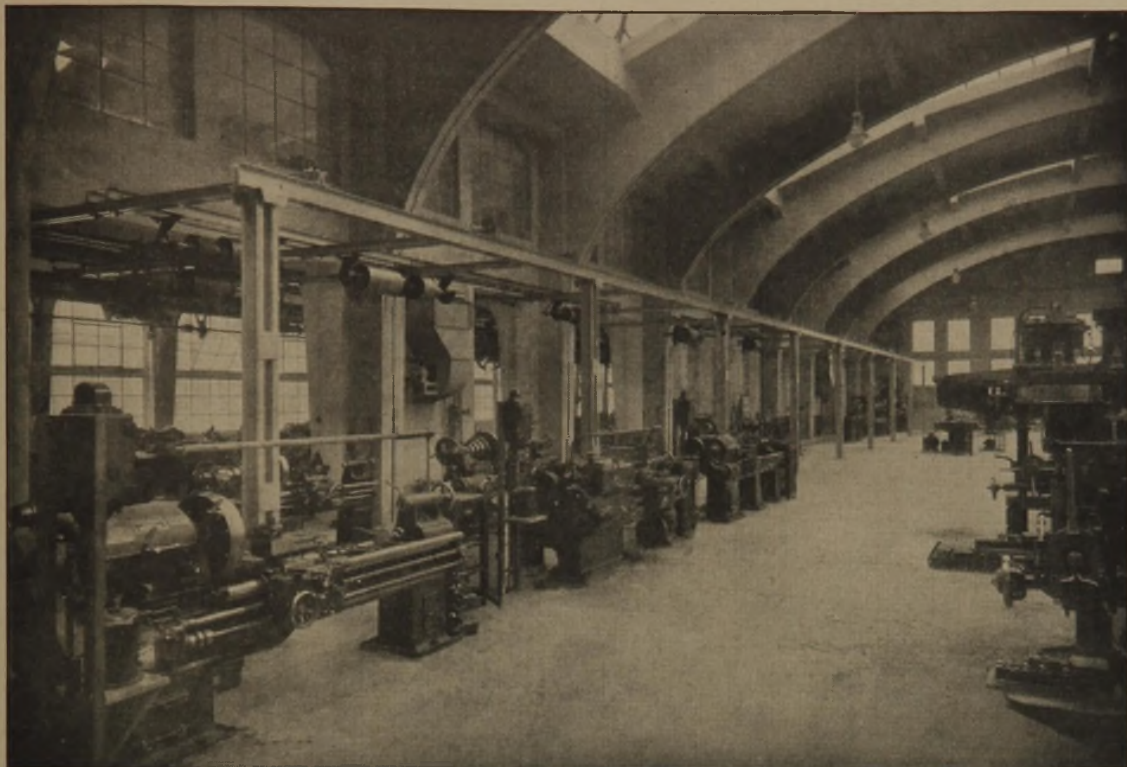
Werkhalle (Werkzeugmaschinenraum).
